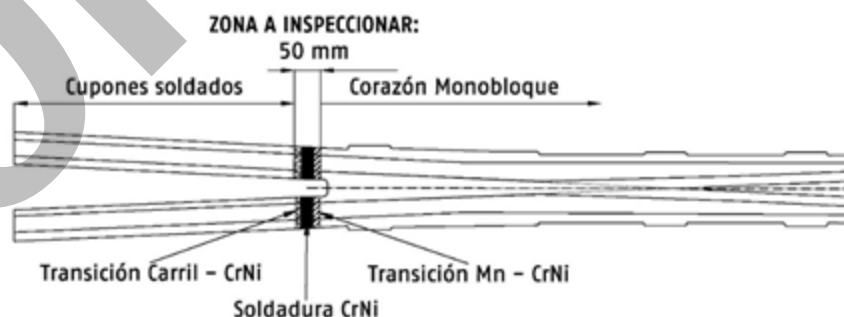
Zona de inspección de soldaduras mediante líquidos penetrantes.
